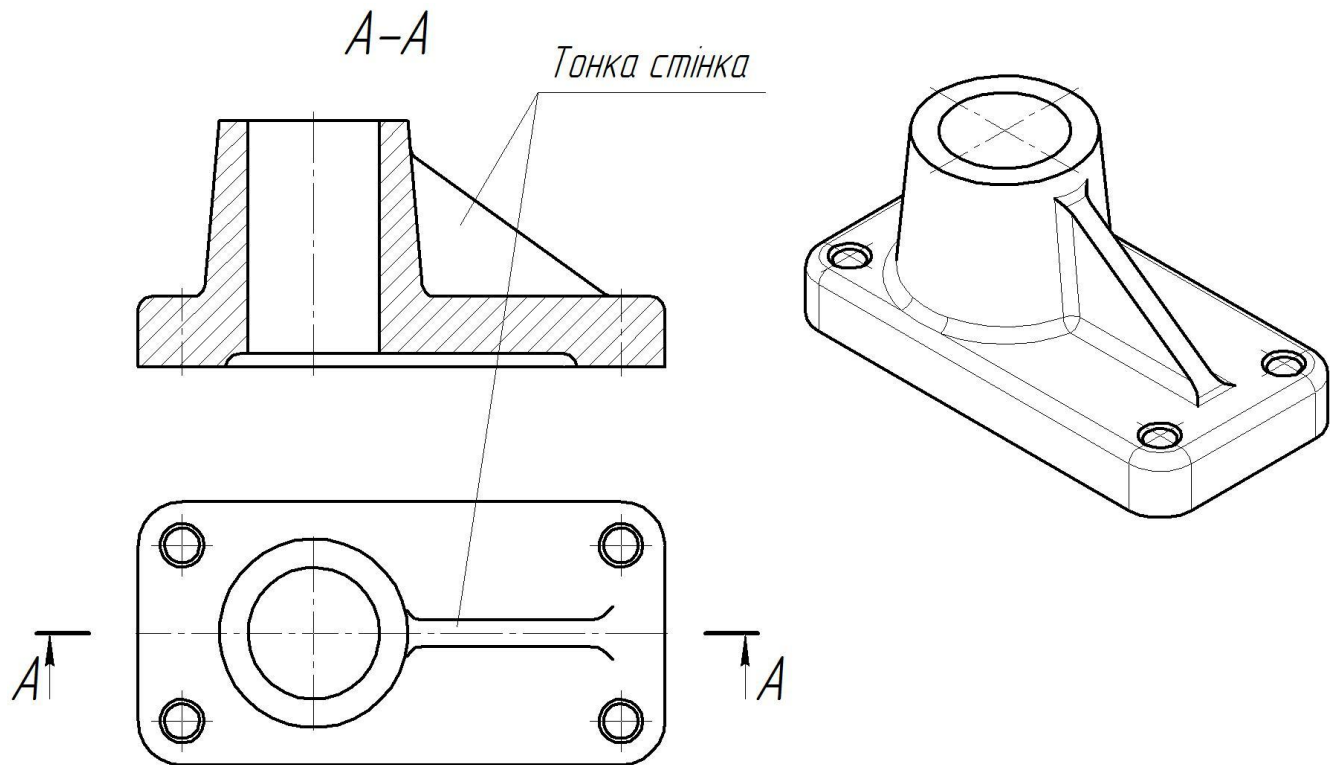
Тонка стінка в розрізі на кресленні
